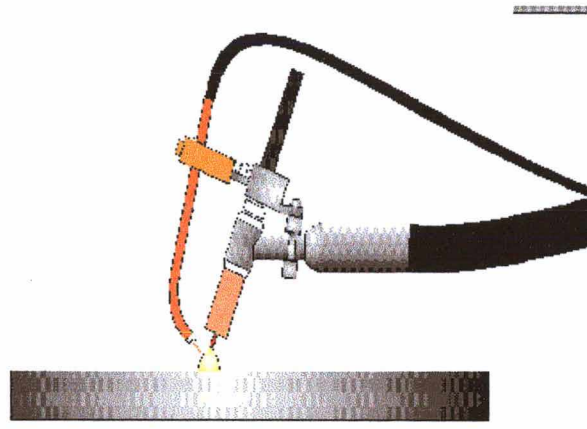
Desenho esquemático da tocha TIG com suporte adaptador.
